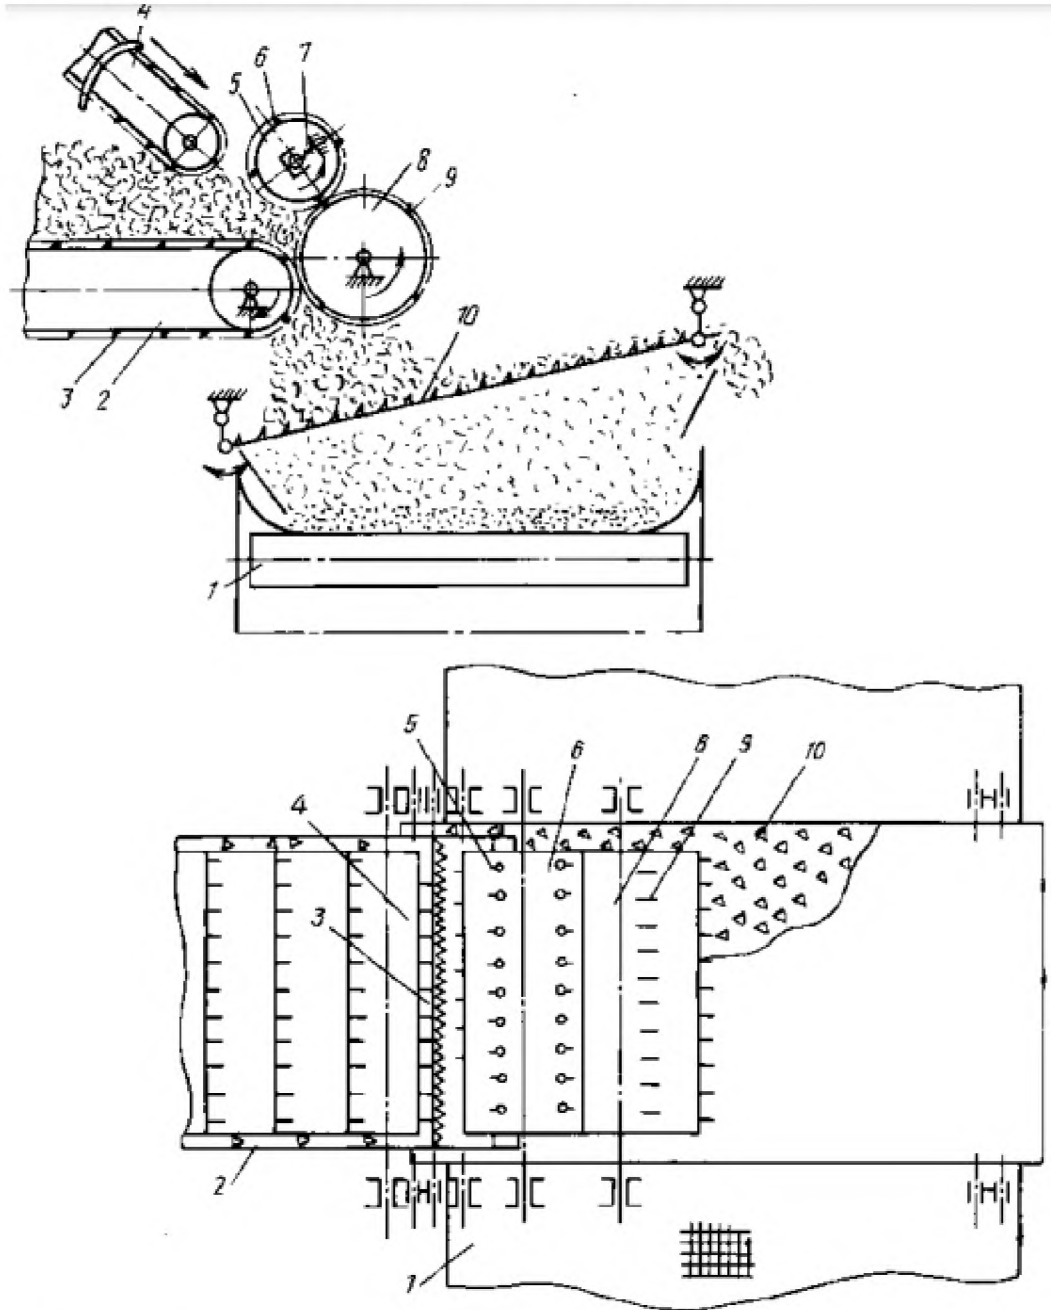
Пристрій для відділення грубих домішок: 1 – конвеєр; 2 – транспортер, що подає; 3 – планки; 4 - транспортер-вирівнювач; 5 - пружний каток; 6 – конусні зубці; 7 – пружина; 8 – завантажувальний барабан; 9 – серпоподібні зуби; 10 – грохот.
